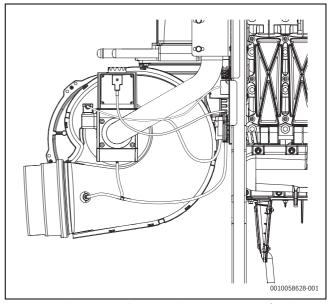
Ventilatore con collegamento di ingresso aria 500/620 kW
